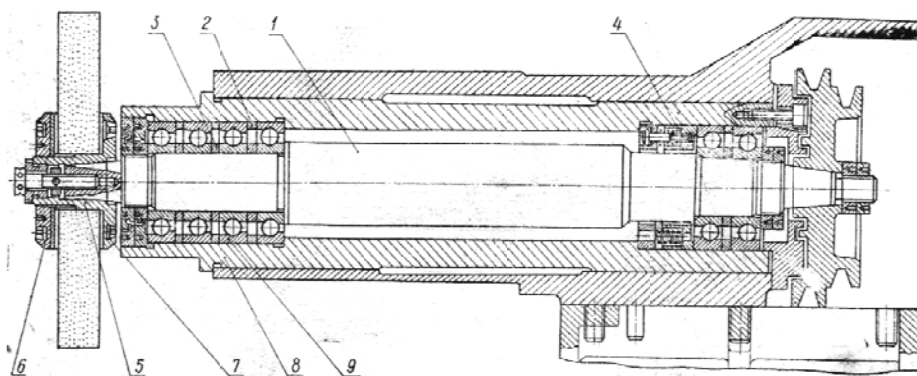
Вид шпиндельного узла ведущего круга бесцентрово-шлифовального станка
